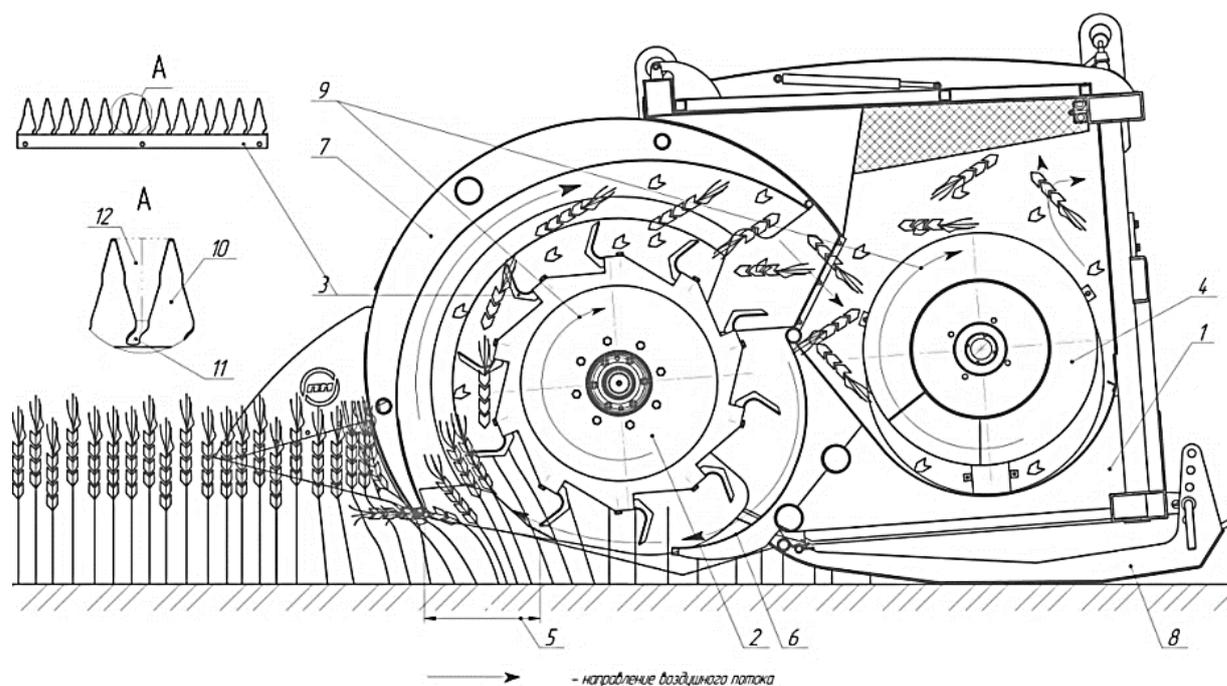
Технологическая схема работы однороторной жатки с новой конструкцией очёсывающего ротора:
